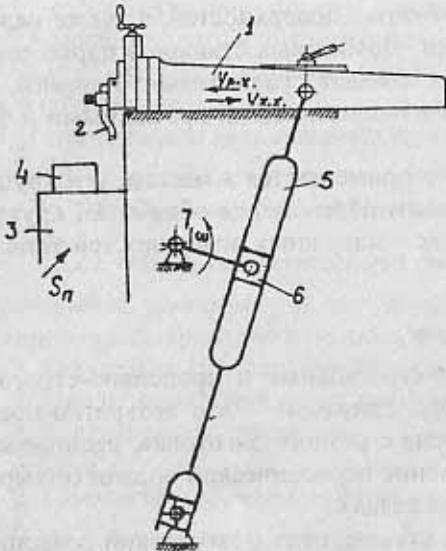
Схема привода ползуна поперечно-строгального станка с помощью механизма качающейся кулисы:
